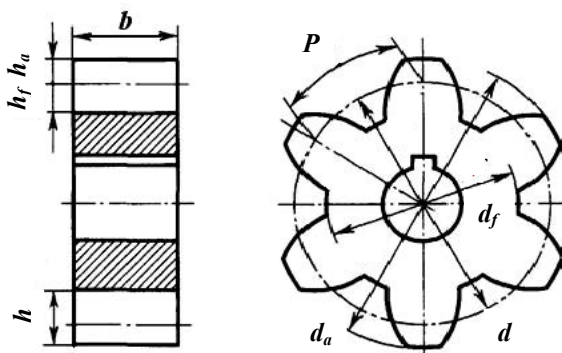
Основные элементы цилиндрического прямозубого зубчатого колеса
